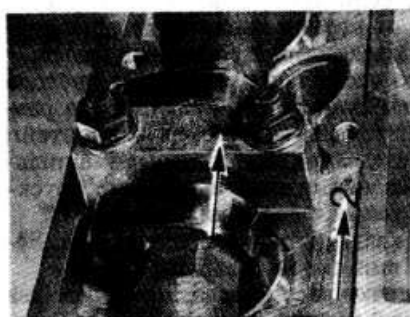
Маркировка (указана стрелкой) на крышке подшипника распредвала и головке блока цилиндров — двигателя с двумя распредвалами
